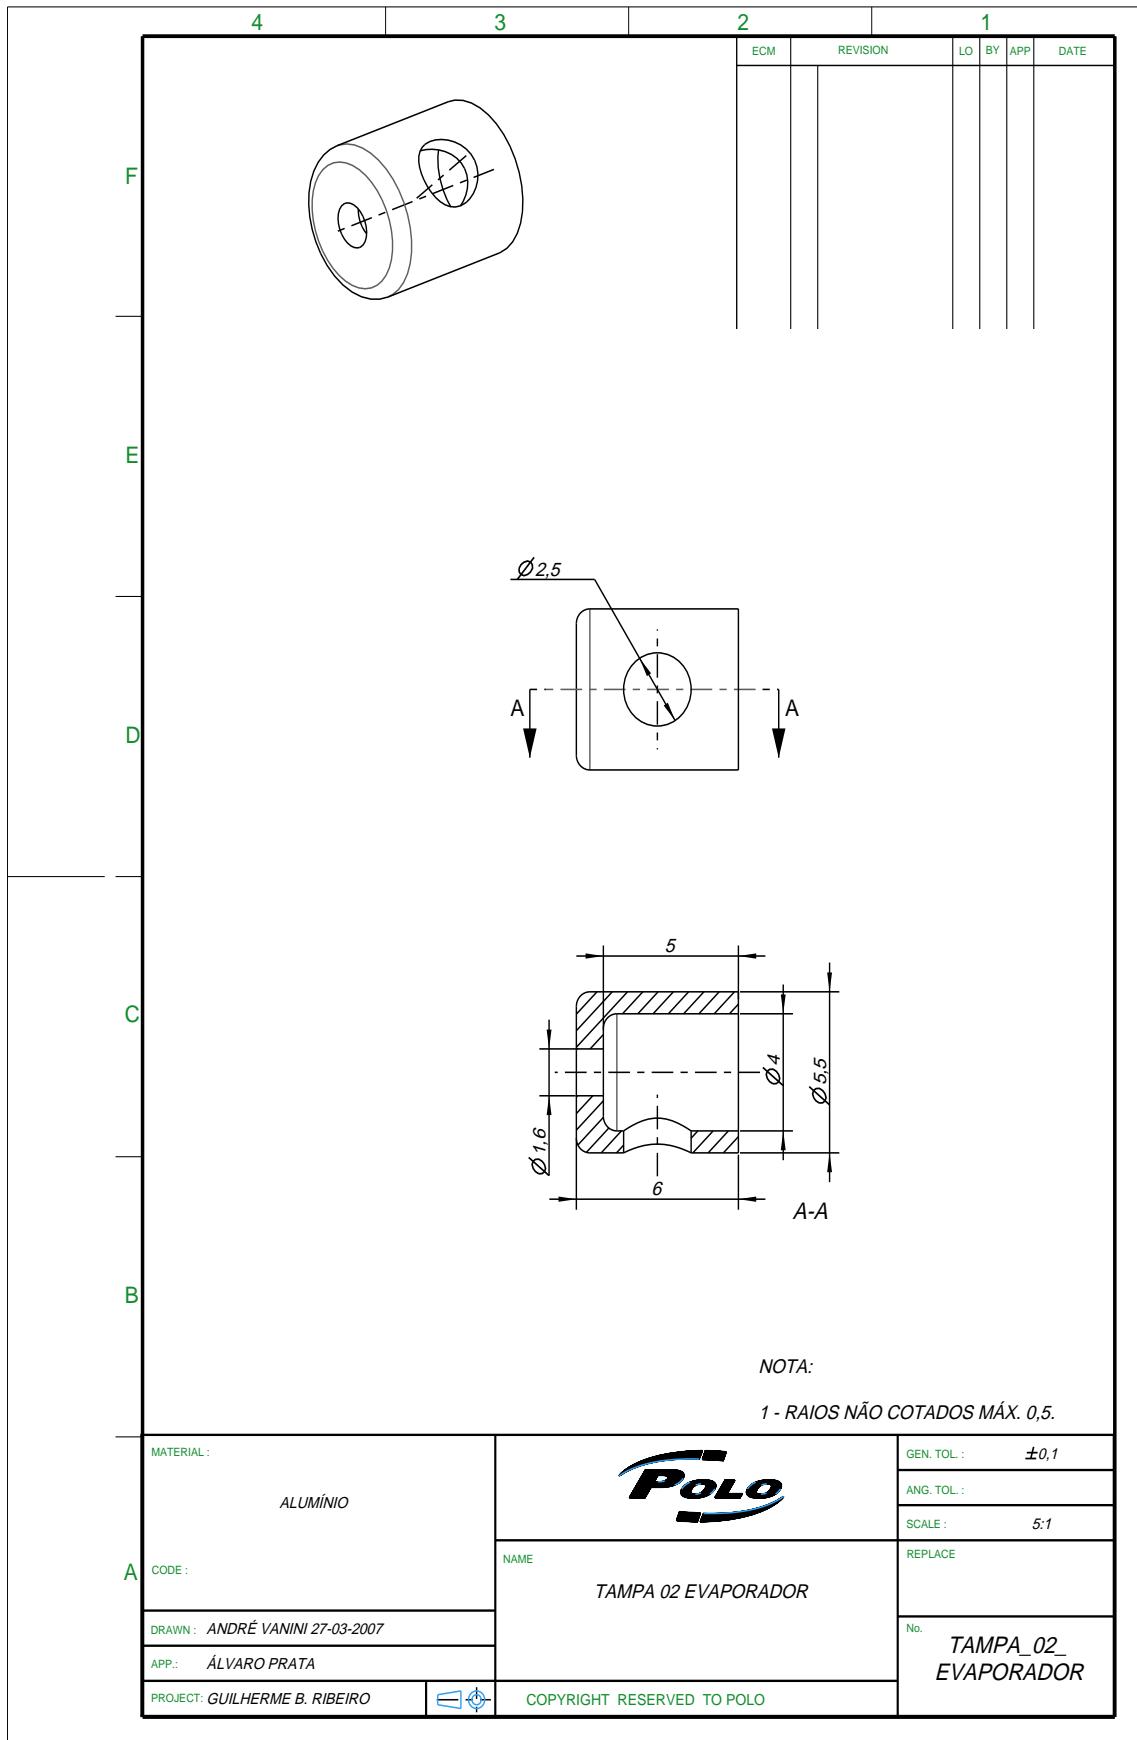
Desenho técnico do evaporador acoplado a tubos de calor - Parte IV
